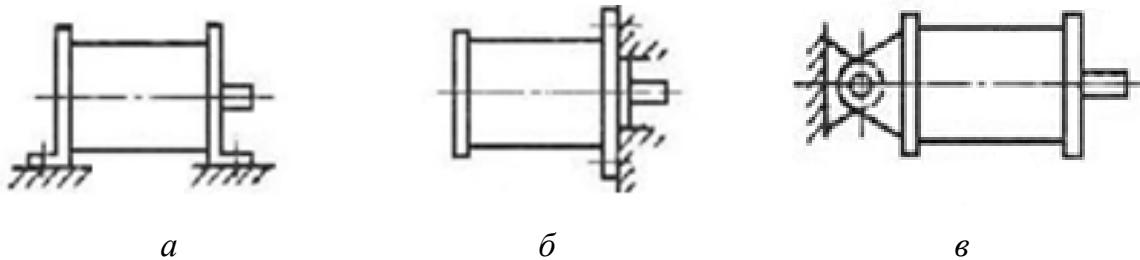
Виды пневмодвигателей в зависимости от способа их крепления к корпусу приспособления:
